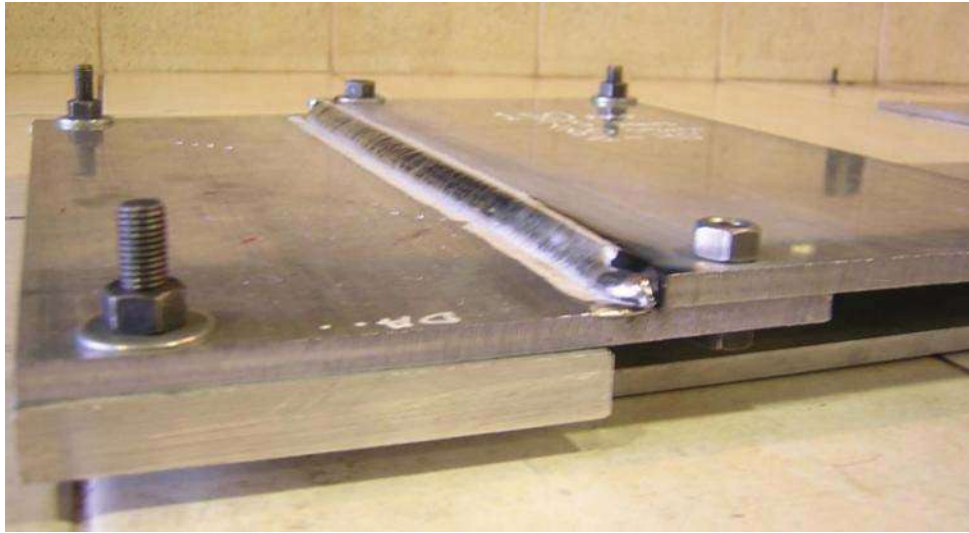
Apariencia de una soldadura obtenida con un ángulo de 50°, 150 A y 30 cm/min.
